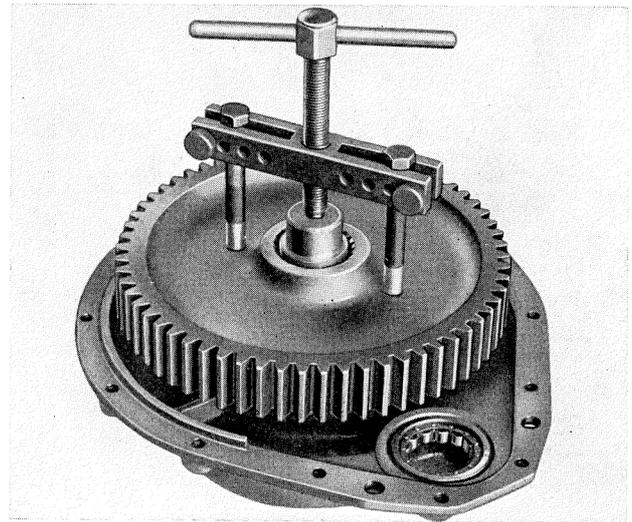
Démontage de la grande roue dentée du réducteur à l'aide de l'extracteur universel et de deux vis (16 MB x 1,5 mm).
